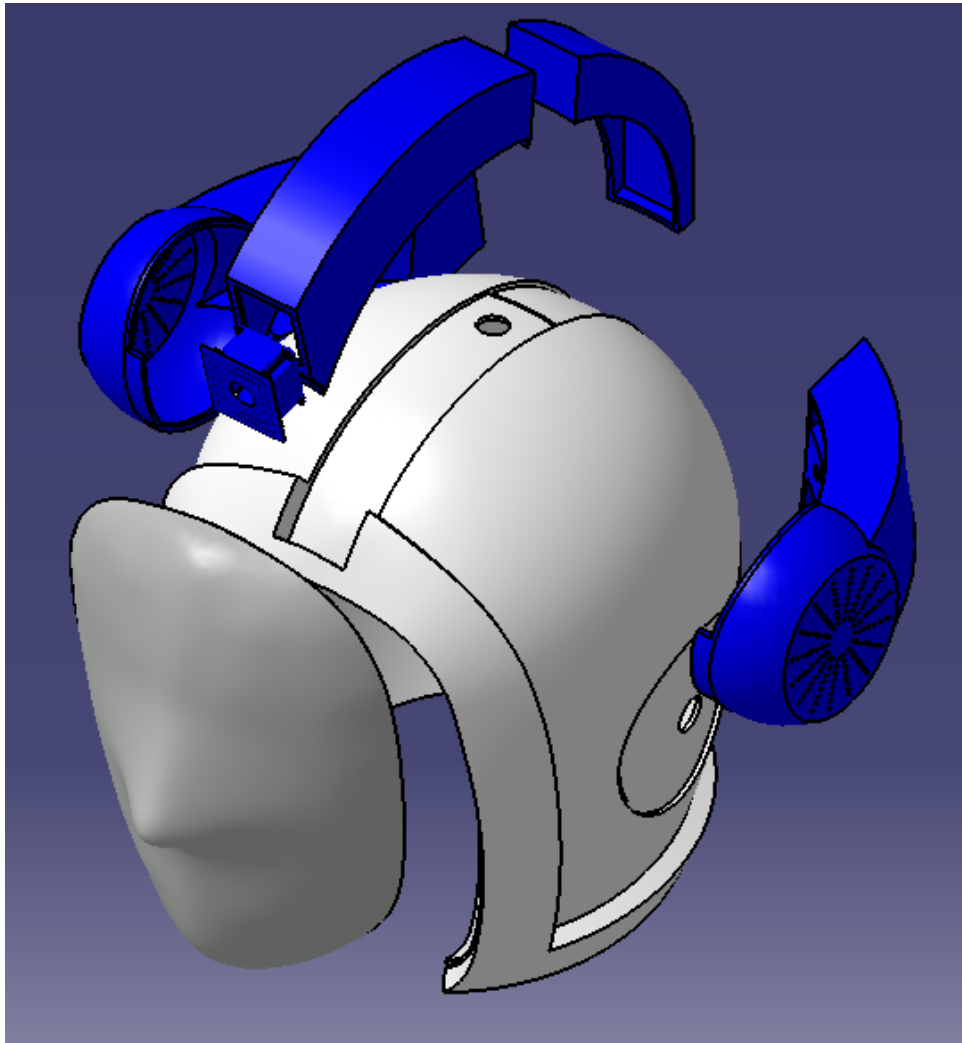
Despiece del conjunto de piezas del subensamblaje casco.
